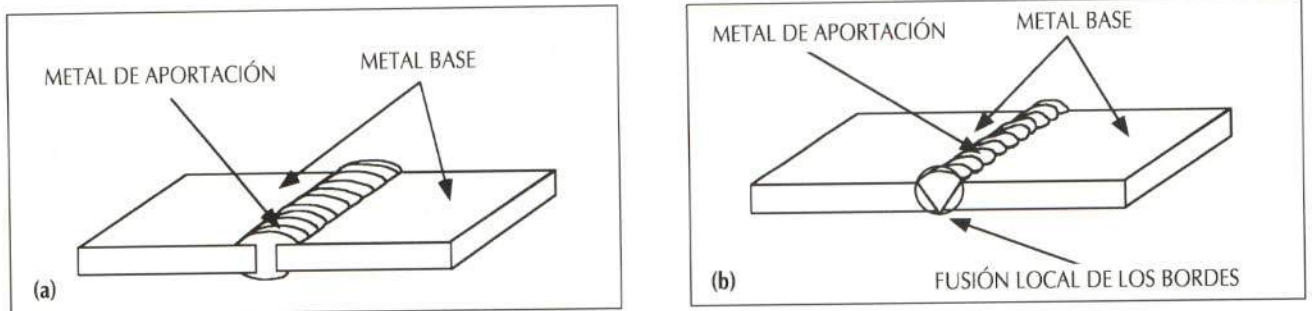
Diferencias entre una unión con soldadura fuerte (a) y una junta soldada (b).
